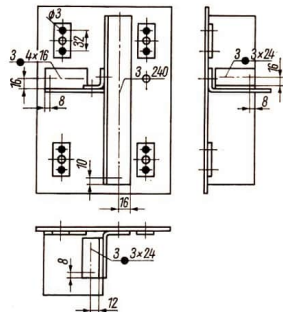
Schweißzeichnung (Schmelzschweißung) nach [4]
